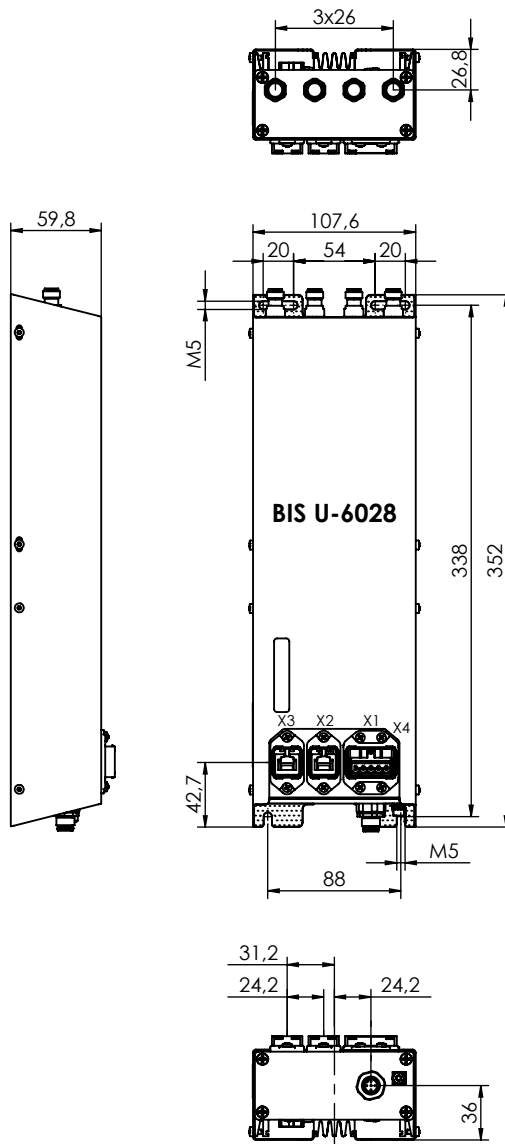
dimensões BIS U-6028-...-ST22 (em mm)
